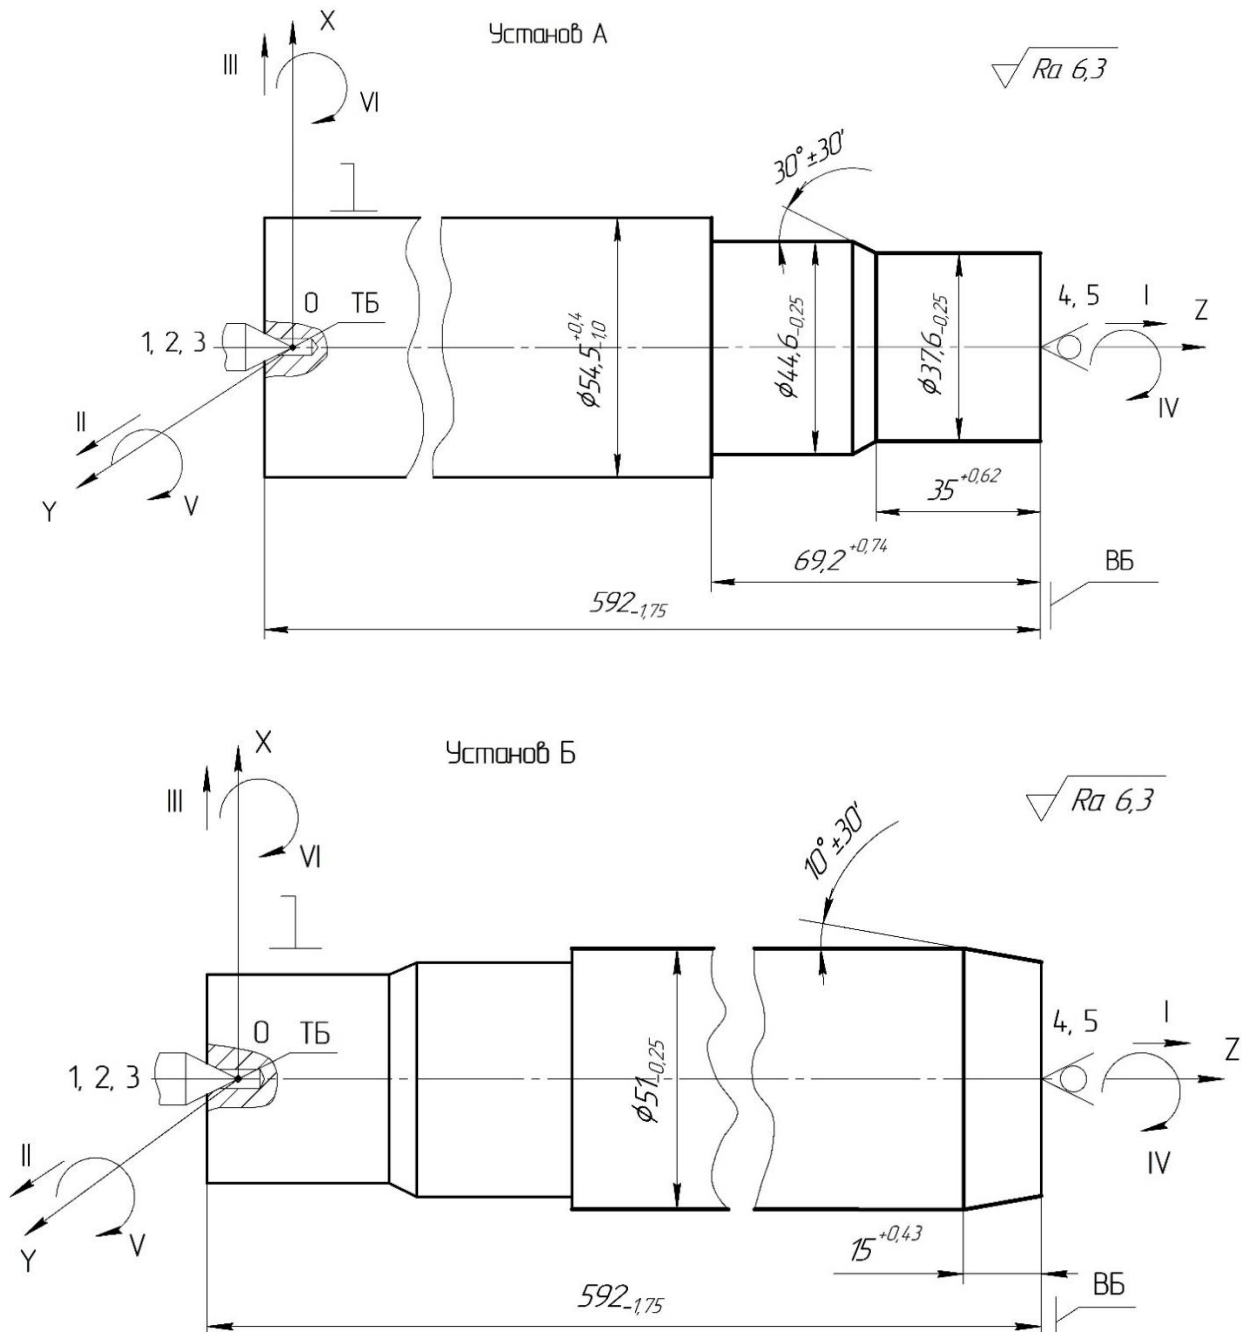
Ескізи заготовки на операції 015 (установи А і Б). Схема № 2
